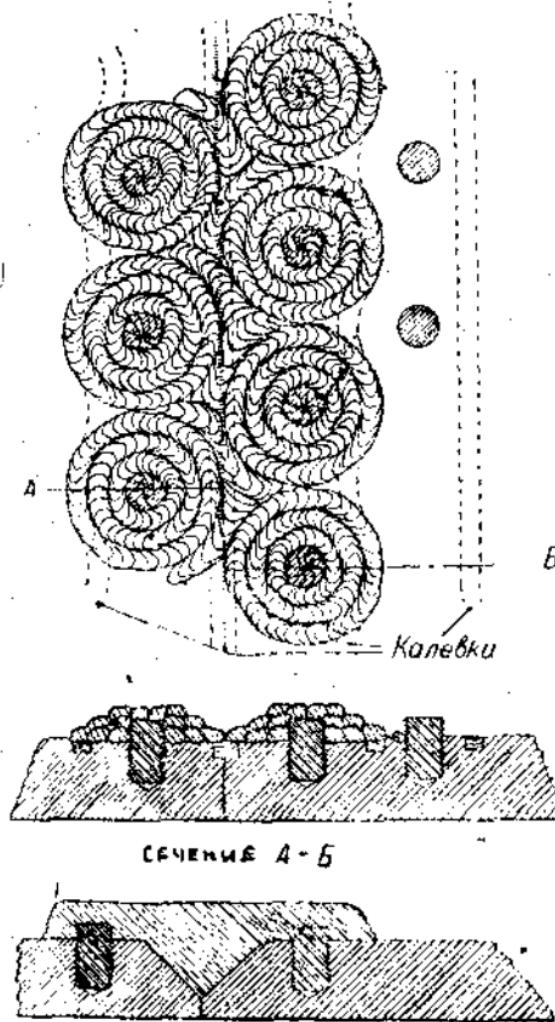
Подготовка чугуна к сварке металлической дугой.
